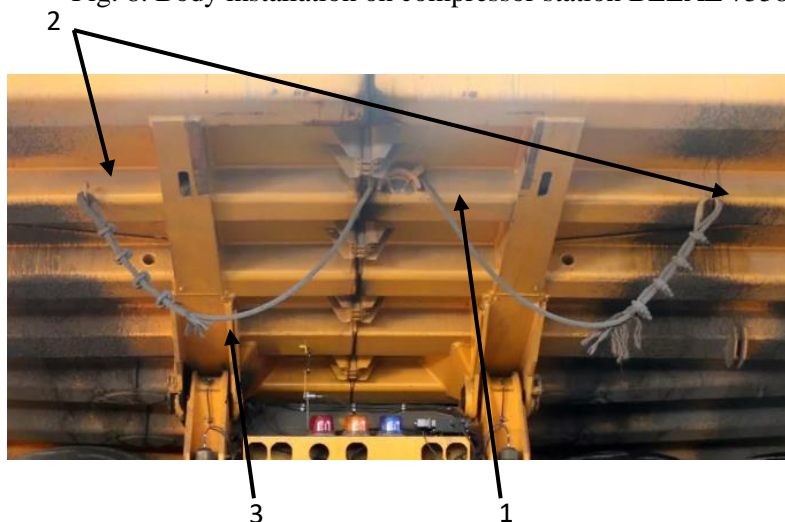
Приспособления для стопорения платформы: 1 – несущий кронштейн; 2 – крюки; 3 – трос
